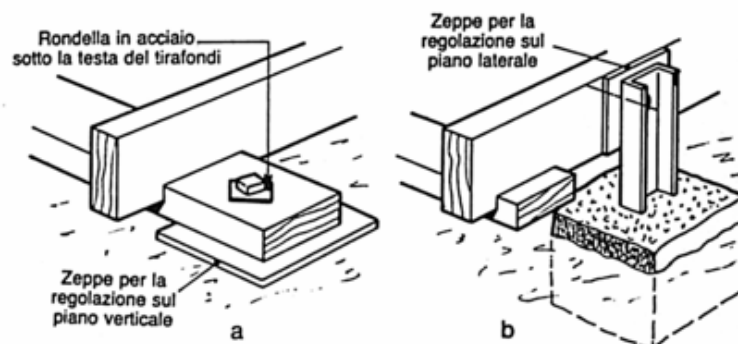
Due esempi di fissaggio dello scalo al pavimento: a. con tirafondi su pavimento duro (tavole o cemento). La regolazione sul piano orizzontale si fa per mezzo di zeppe; b. su ferri ad U immobilizzati in una gettata di cemento. La regolazione sul piano verticale si fa con serraggiunti. I fori dei bulloni saranno eseguiti dopo la regolazione. Le zeppe verticali servono a correggere gli spostamenti fra i ferri opposti.
